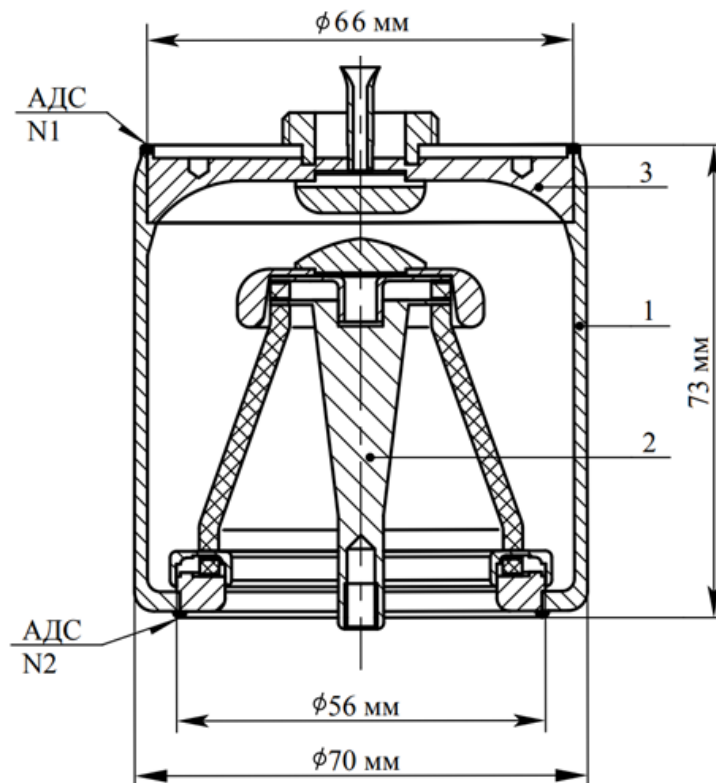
Конструкция разрядника-обострителя РО-49
